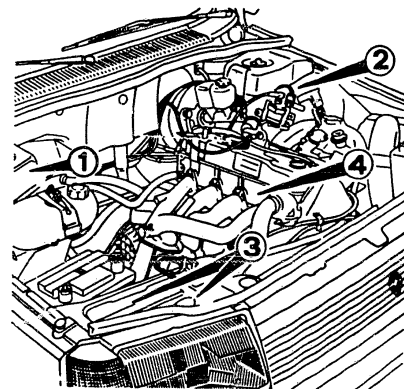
Fahrzeug-Identifikation im Motorraum: 1 Chassisnummer – 2 Farbnummer – 3 Typenschilder – 4 Motornummer.
